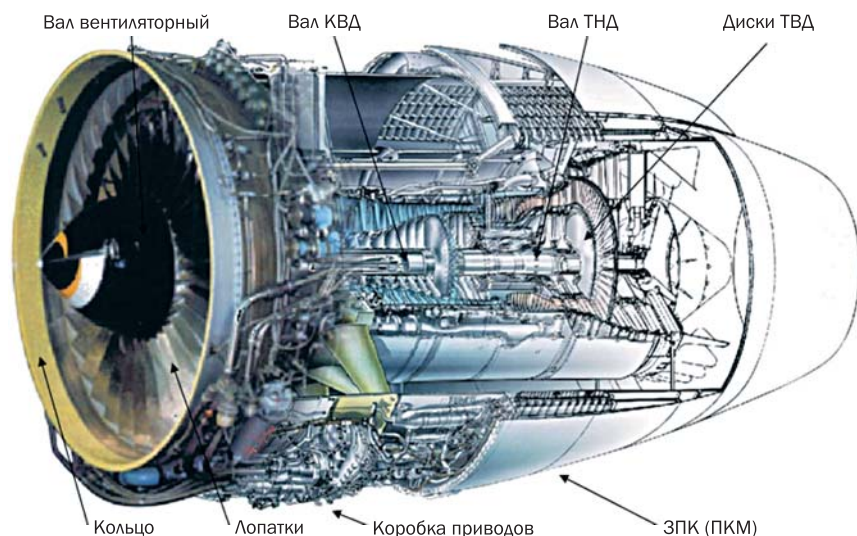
Двигатель ПС-90А. Детали и узлы, подлежащие акустическому контролю
